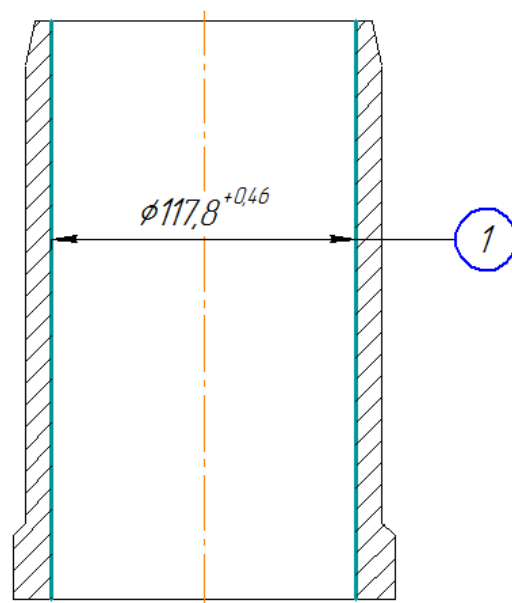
Ескіз обробки заготовки на операції 010
